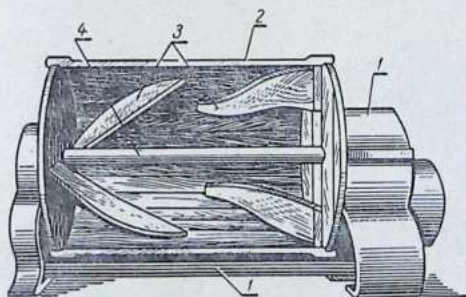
Безвальцовый маслоизготовитель с деревянной бочкой:
